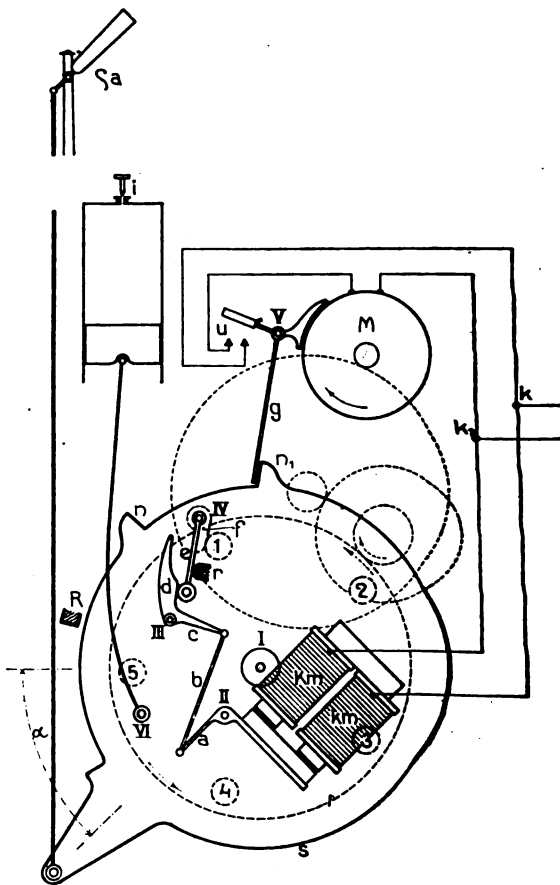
Westinghouse-Antrieb in Grundstellung („Fahrt frei“)
